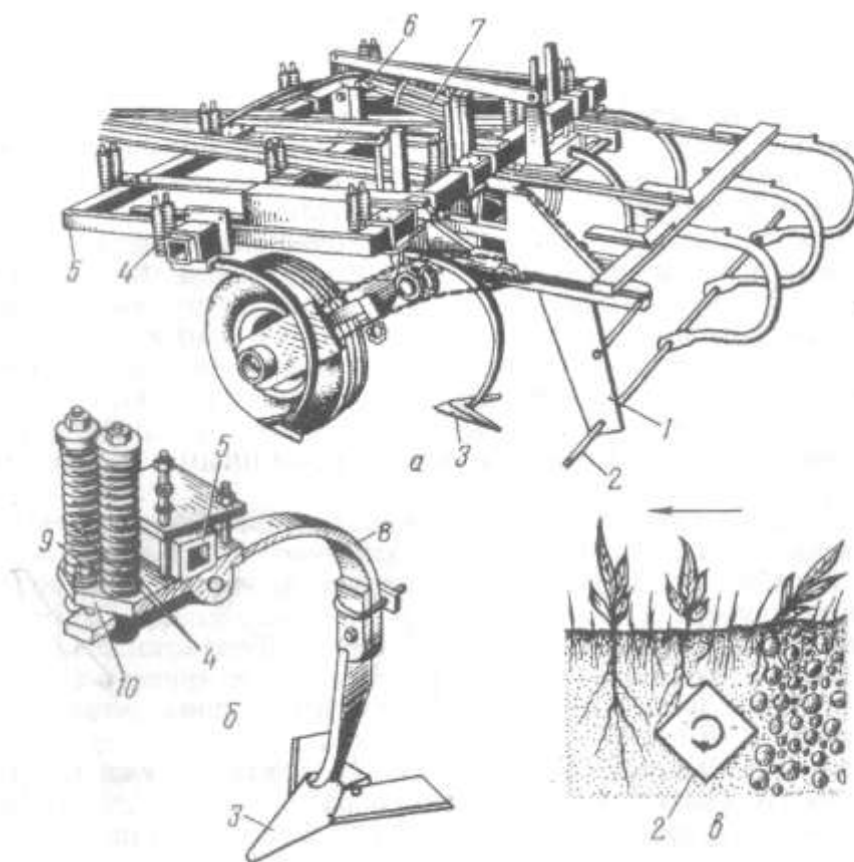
Культиватор КПЭ-3,8А со штанговым приспособлением:
